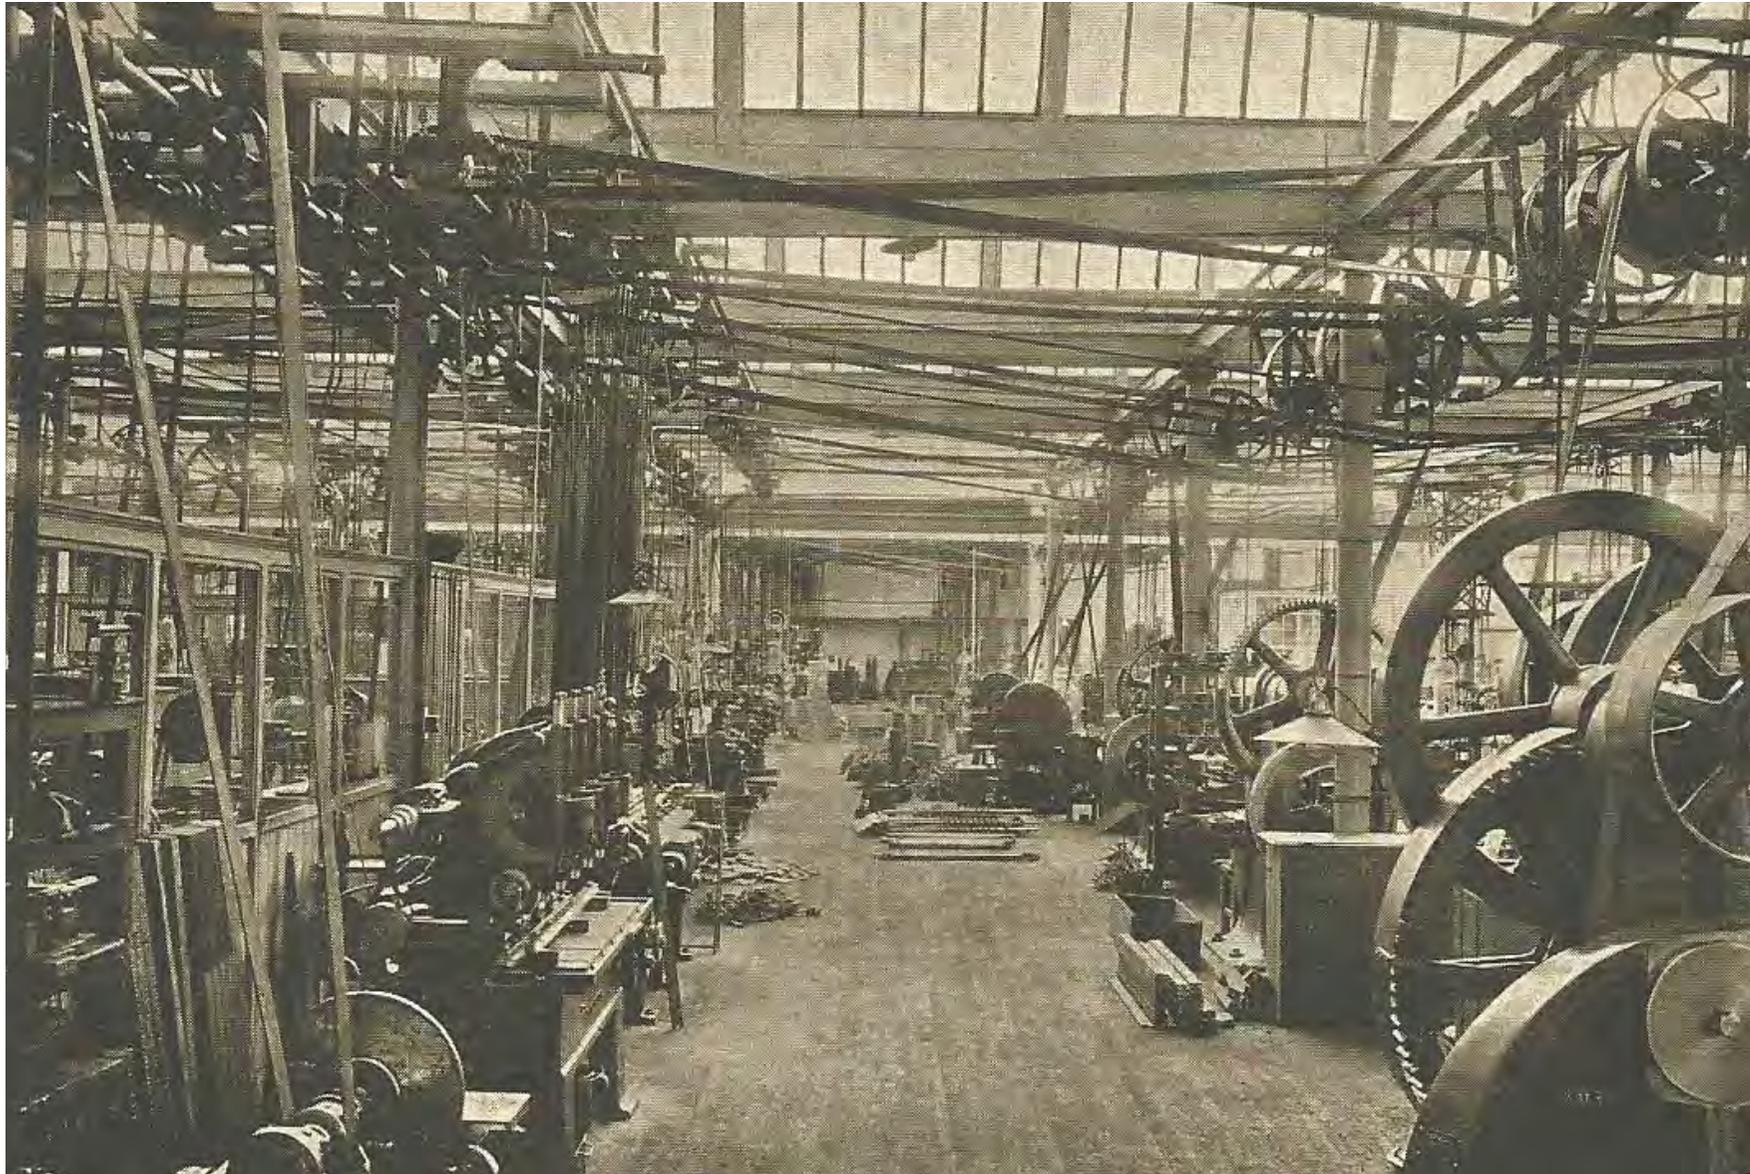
Werkstätten für Bor-, Hobel-, Fräse- und Pressmaschinen (VIII)
